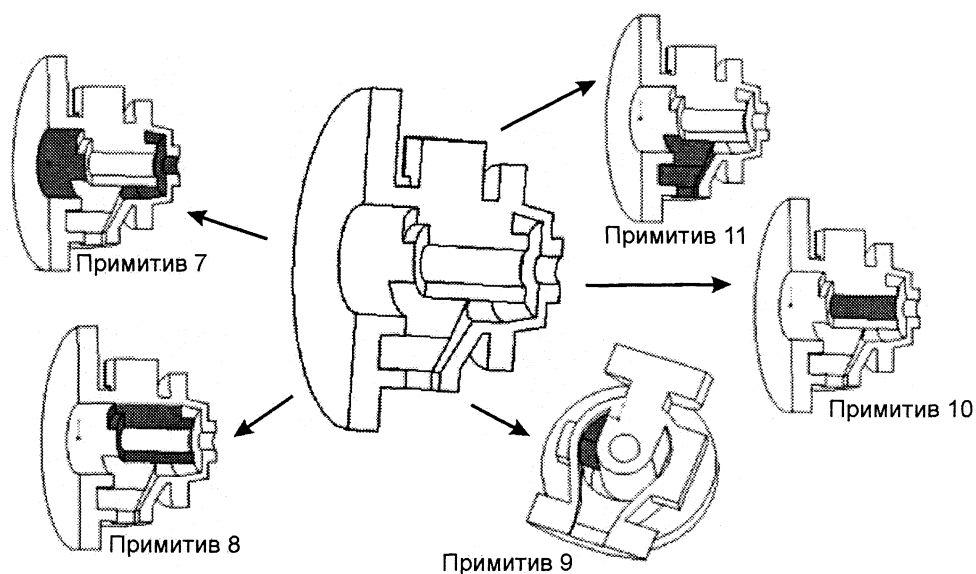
Разделение внутренней поверхности детали «корпус подшипника» на элементарные объекты
